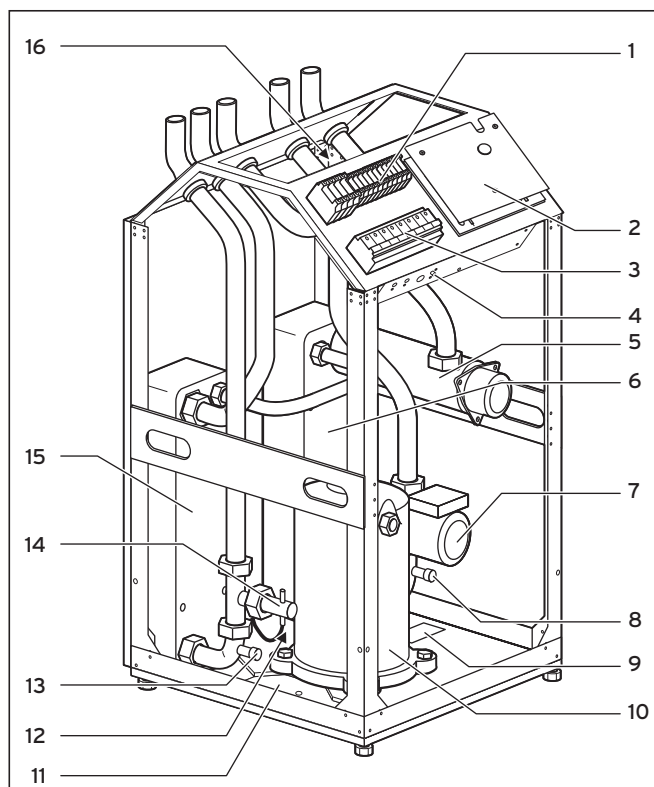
VWW - Vista anteriore con apparecchio aperto
